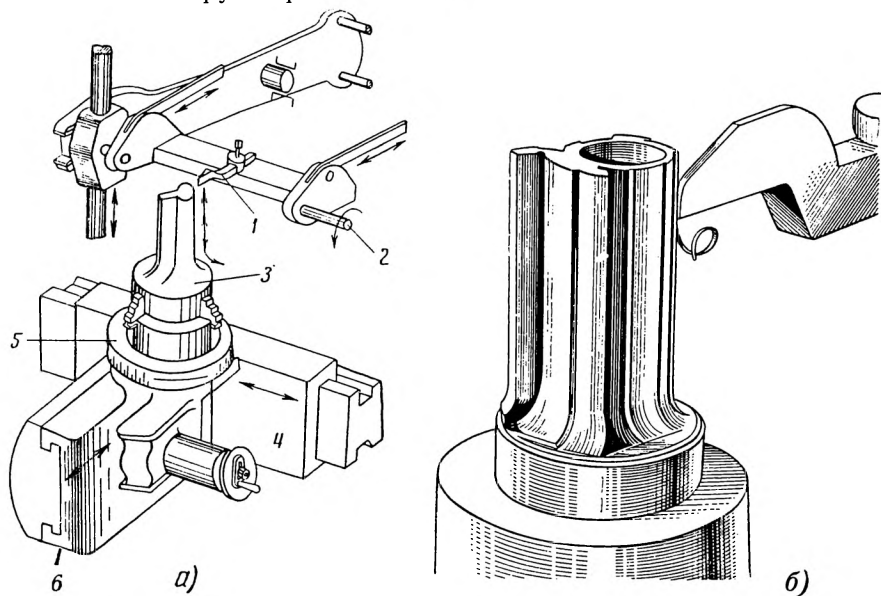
Схема обработки детали сложного профиля на фасонно-строгальном станке (*а*), обрабатываемая деталь и резец в процессе обработки (*б*)
